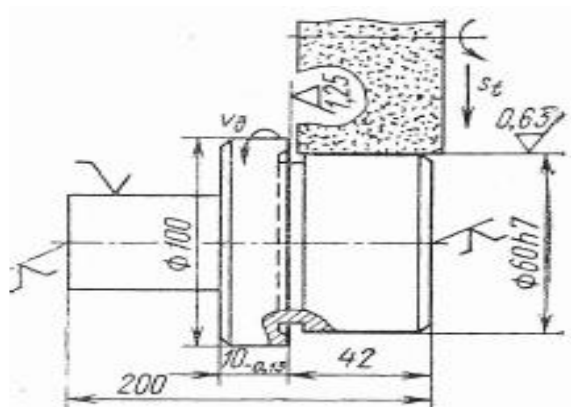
Ескіз круглого шліфування шийки і торця вала
